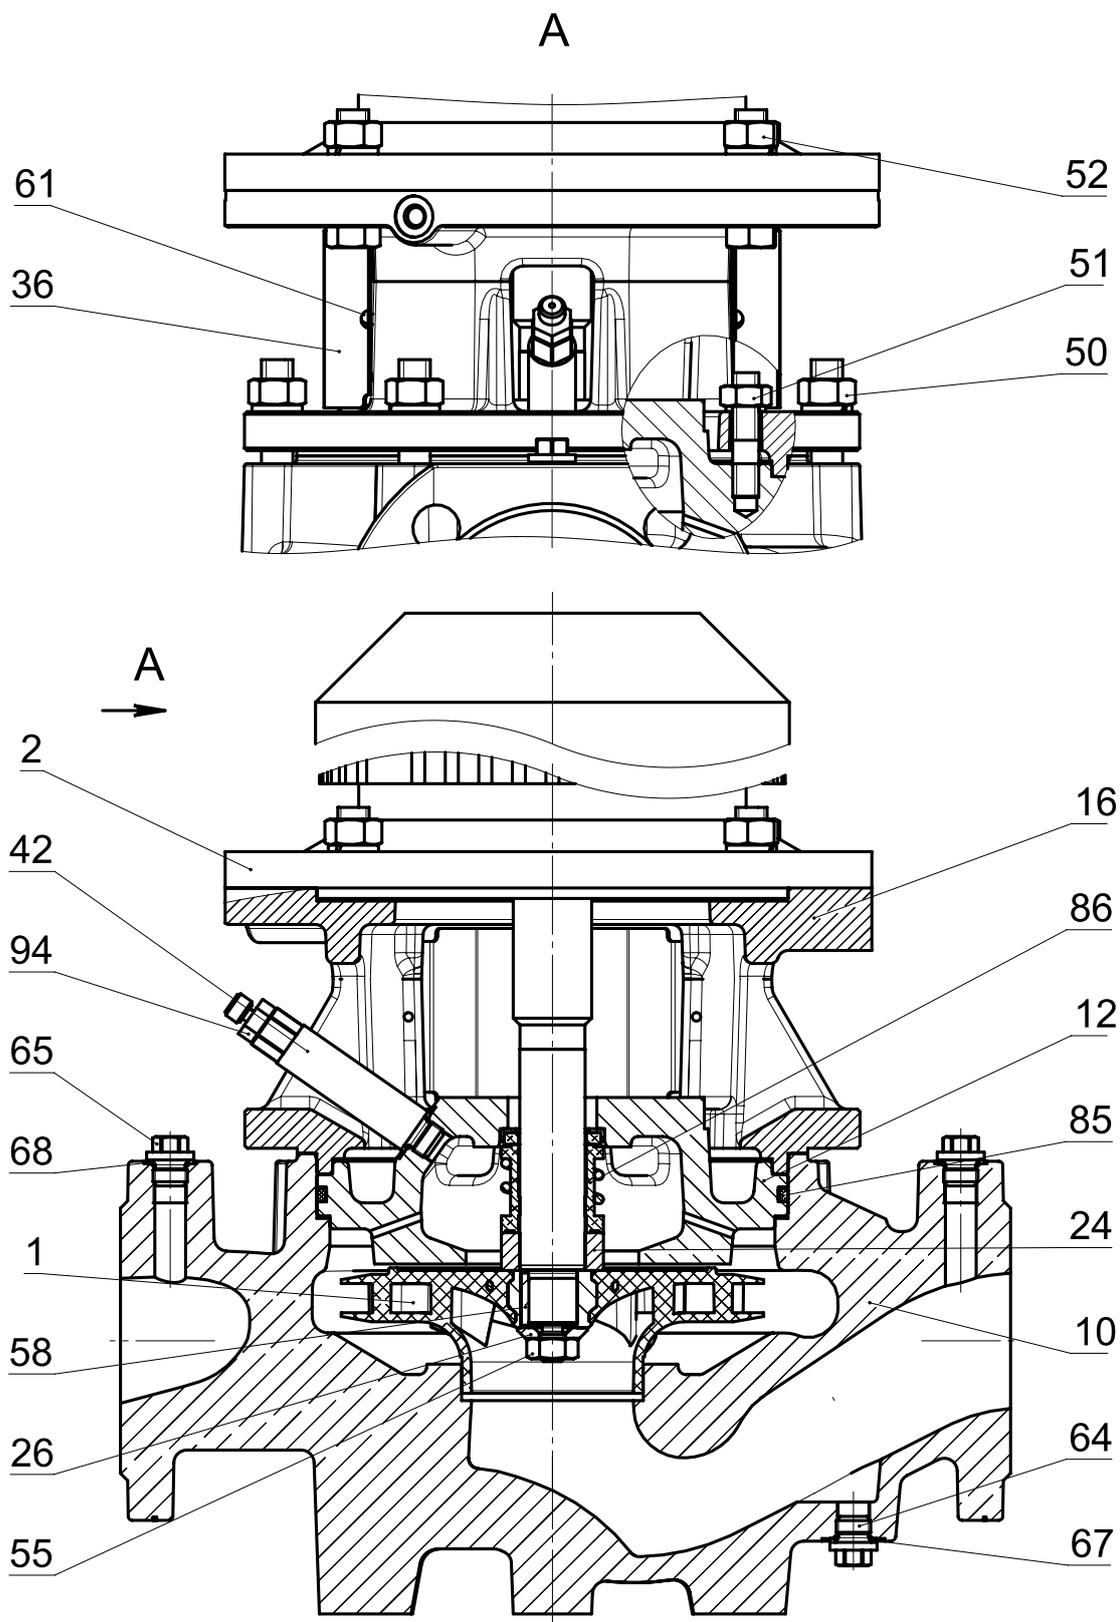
Типоразмеры 32-32-202, 40-40-160, 40-40-200, 50-50-160, 50-50-200, 65-65-160, 65-65-200, 80-80-160, 80-80-200, 125-125-200
